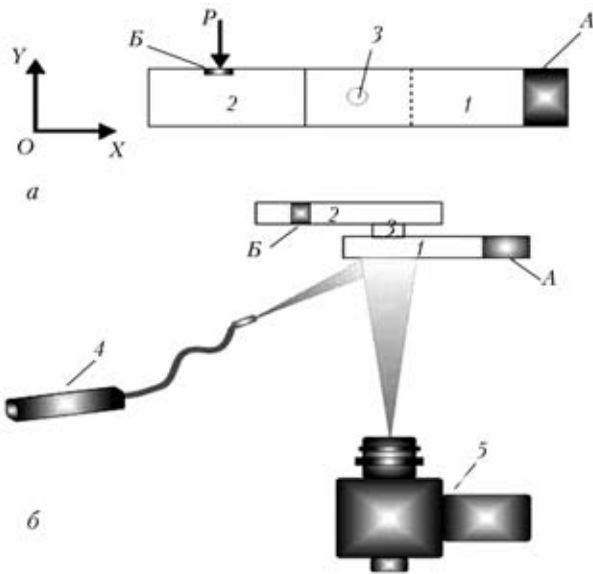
Схема експерименту, який виконувався для кількісної оцінки діаметра ядра зварної точки: а — схема навантаження зразка; б — оптична схема експерименту; 1, 2 — відповідно передня та задня металева смуга; 3 — зварна точка; 4 — лазер із світловодом; 5 — ширографічний модуль (А — зона кріплення зразка; Б — зона прикладення навантаження Р)
